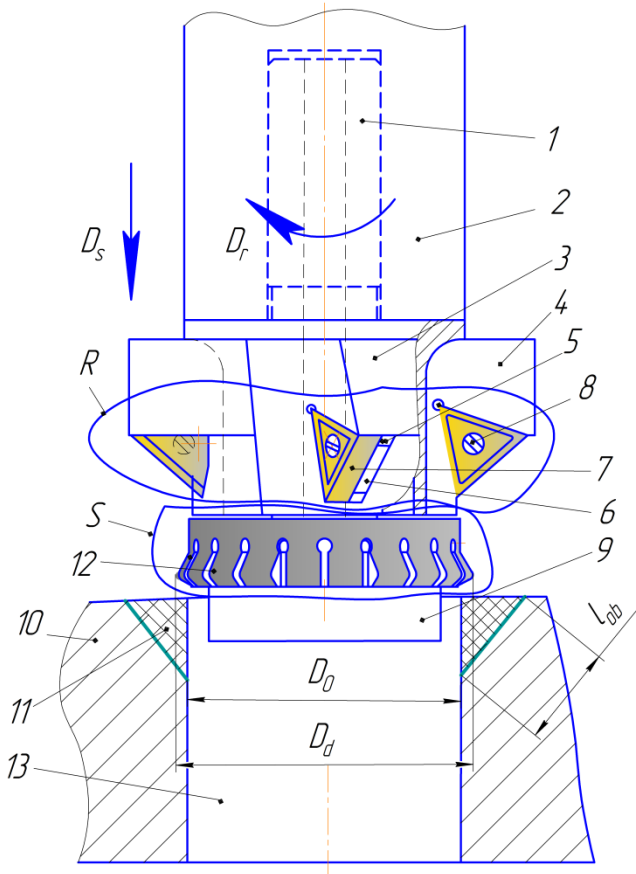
Инструмент, состоящий из режущего и стабилизирующего модулей, перед началом механической обработки наплавленного конического отверстия
